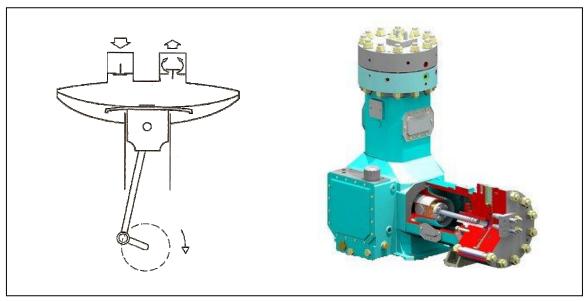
ESQUEMA DE UN COMPRESOR DE DIAFRAGMA (IZQUIERDA); COMPRESOR DE DIAFRAGMA (DERECHA)
